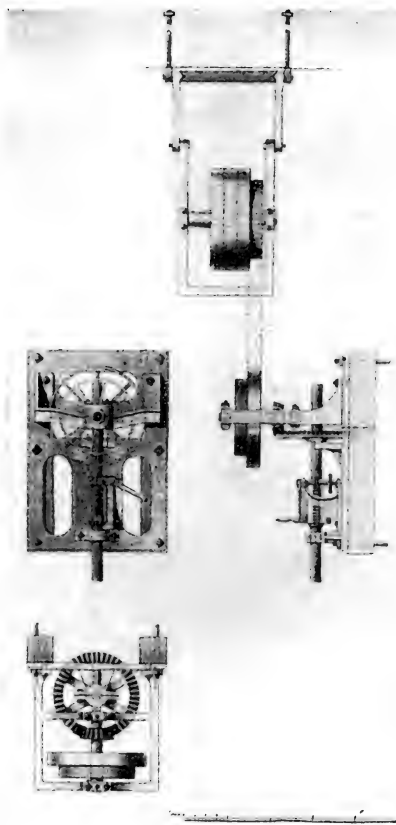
Настенный сверлильный станок Луганского завода 1830 г. Заводской чертеж.
